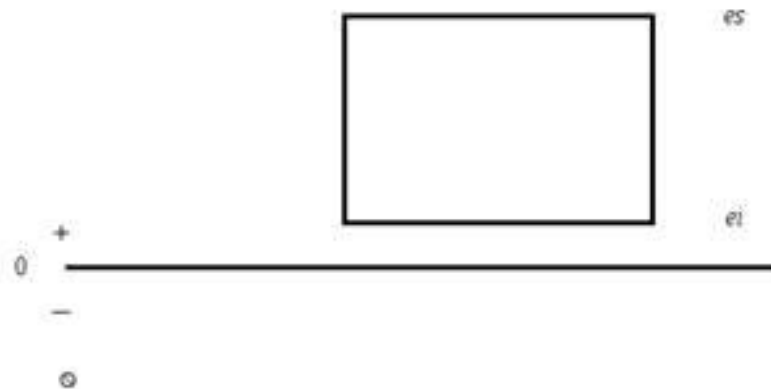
Схема расположения поля допуска вала
